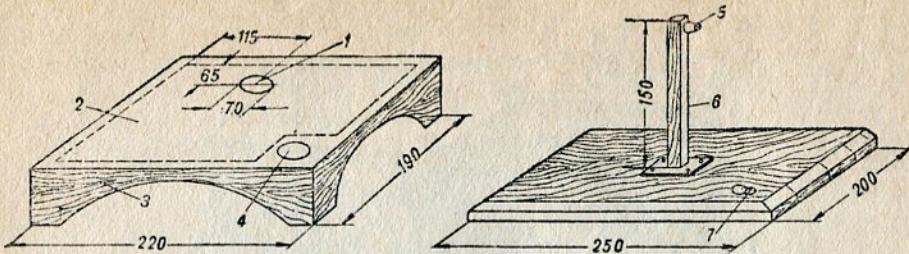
Подставки для разборки, сборки и изучения фотокинопулемета
